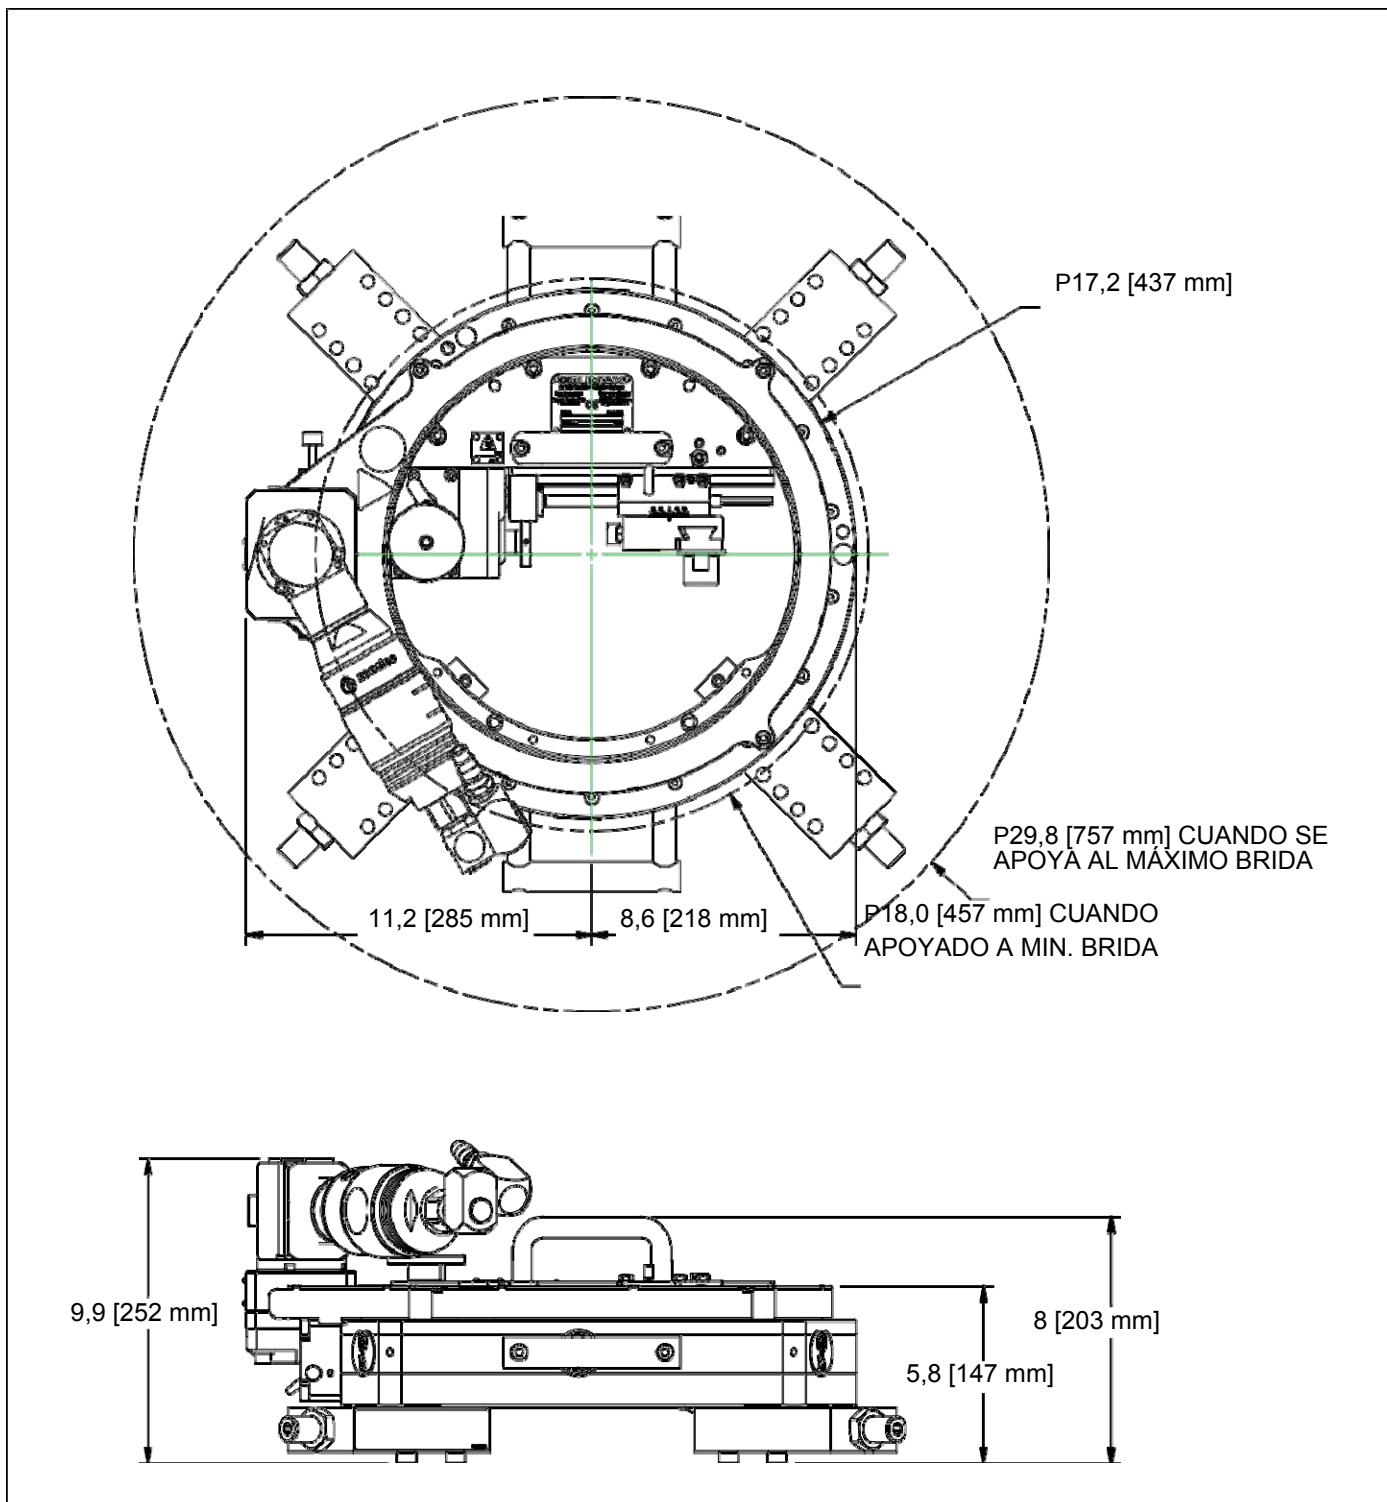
FF2400 DIMENSIONES DE LA MÁQUINA
